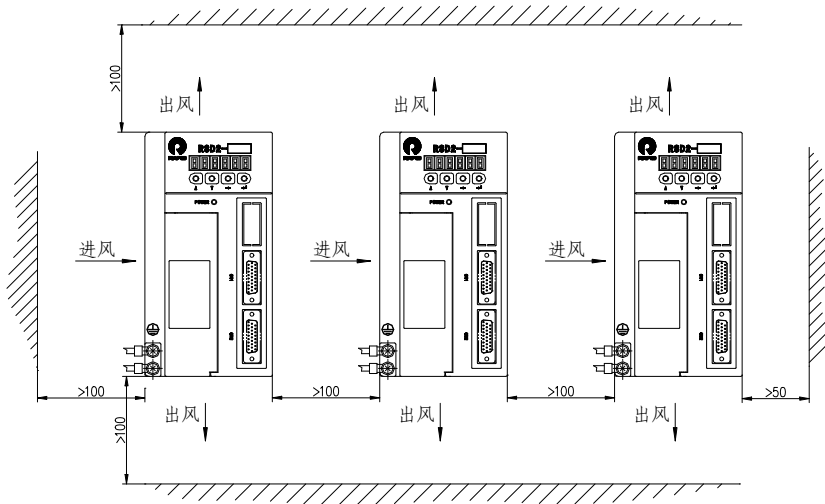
多个驱动器安装时的位置示意图（单位：mm）
